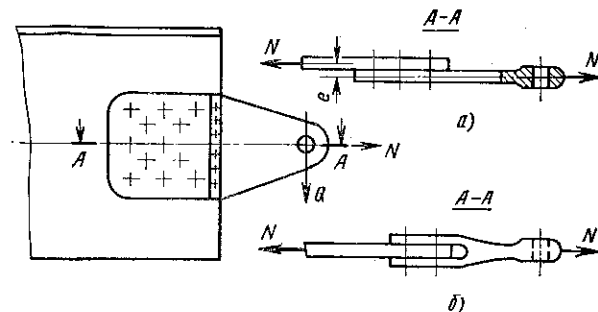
Плоский шарнирный узел крыла, установленный на стенке
